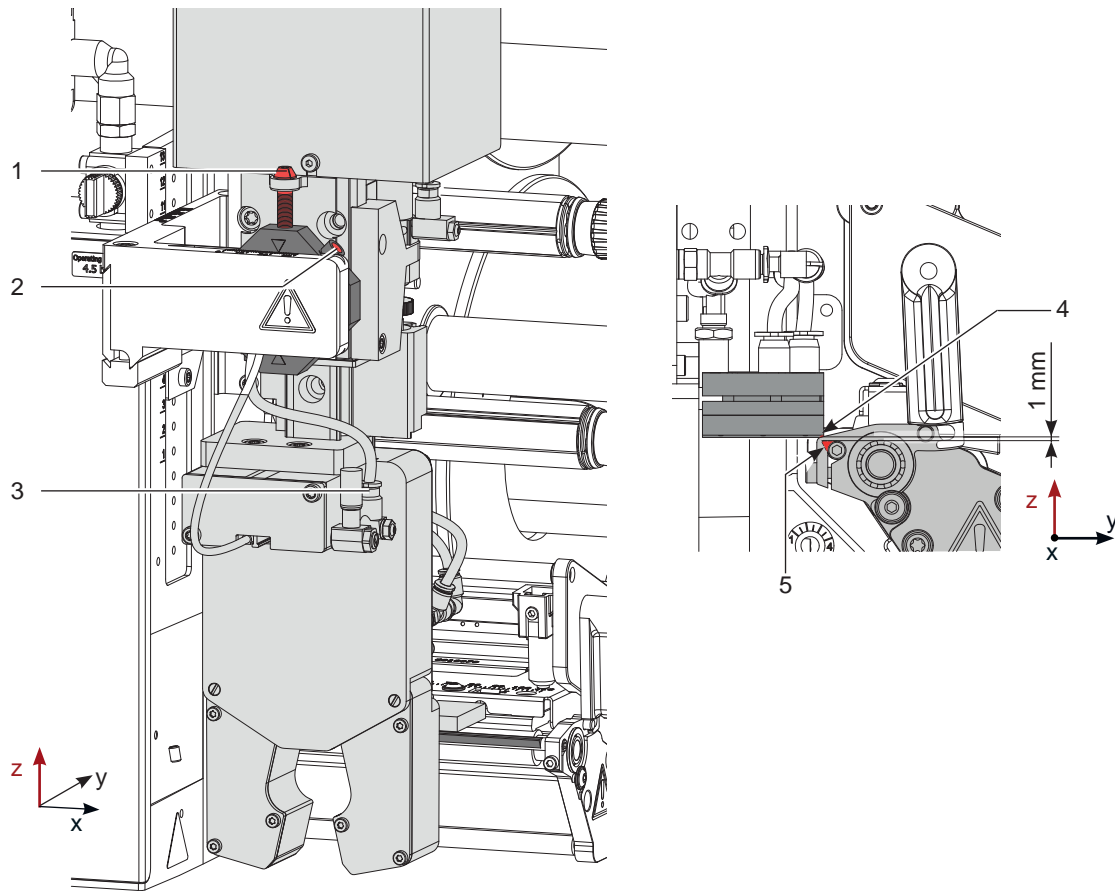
Verschiebung der Stempelbaugruppe in Z-Richtung
